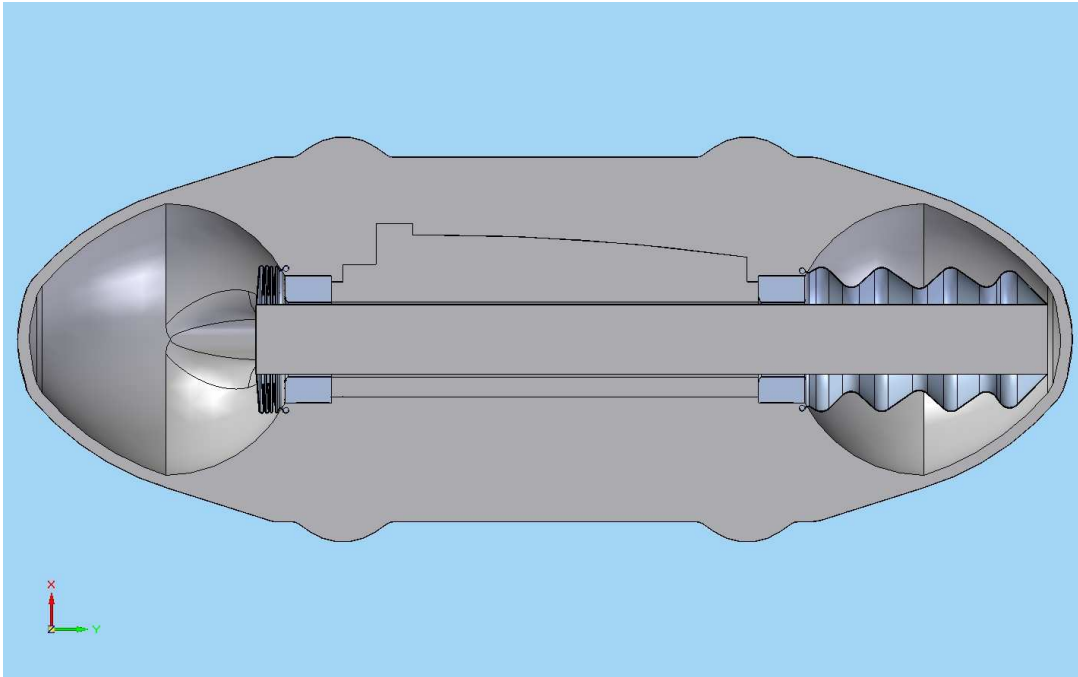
Varianta 1 – priestorový pohľad na čerpadlo
